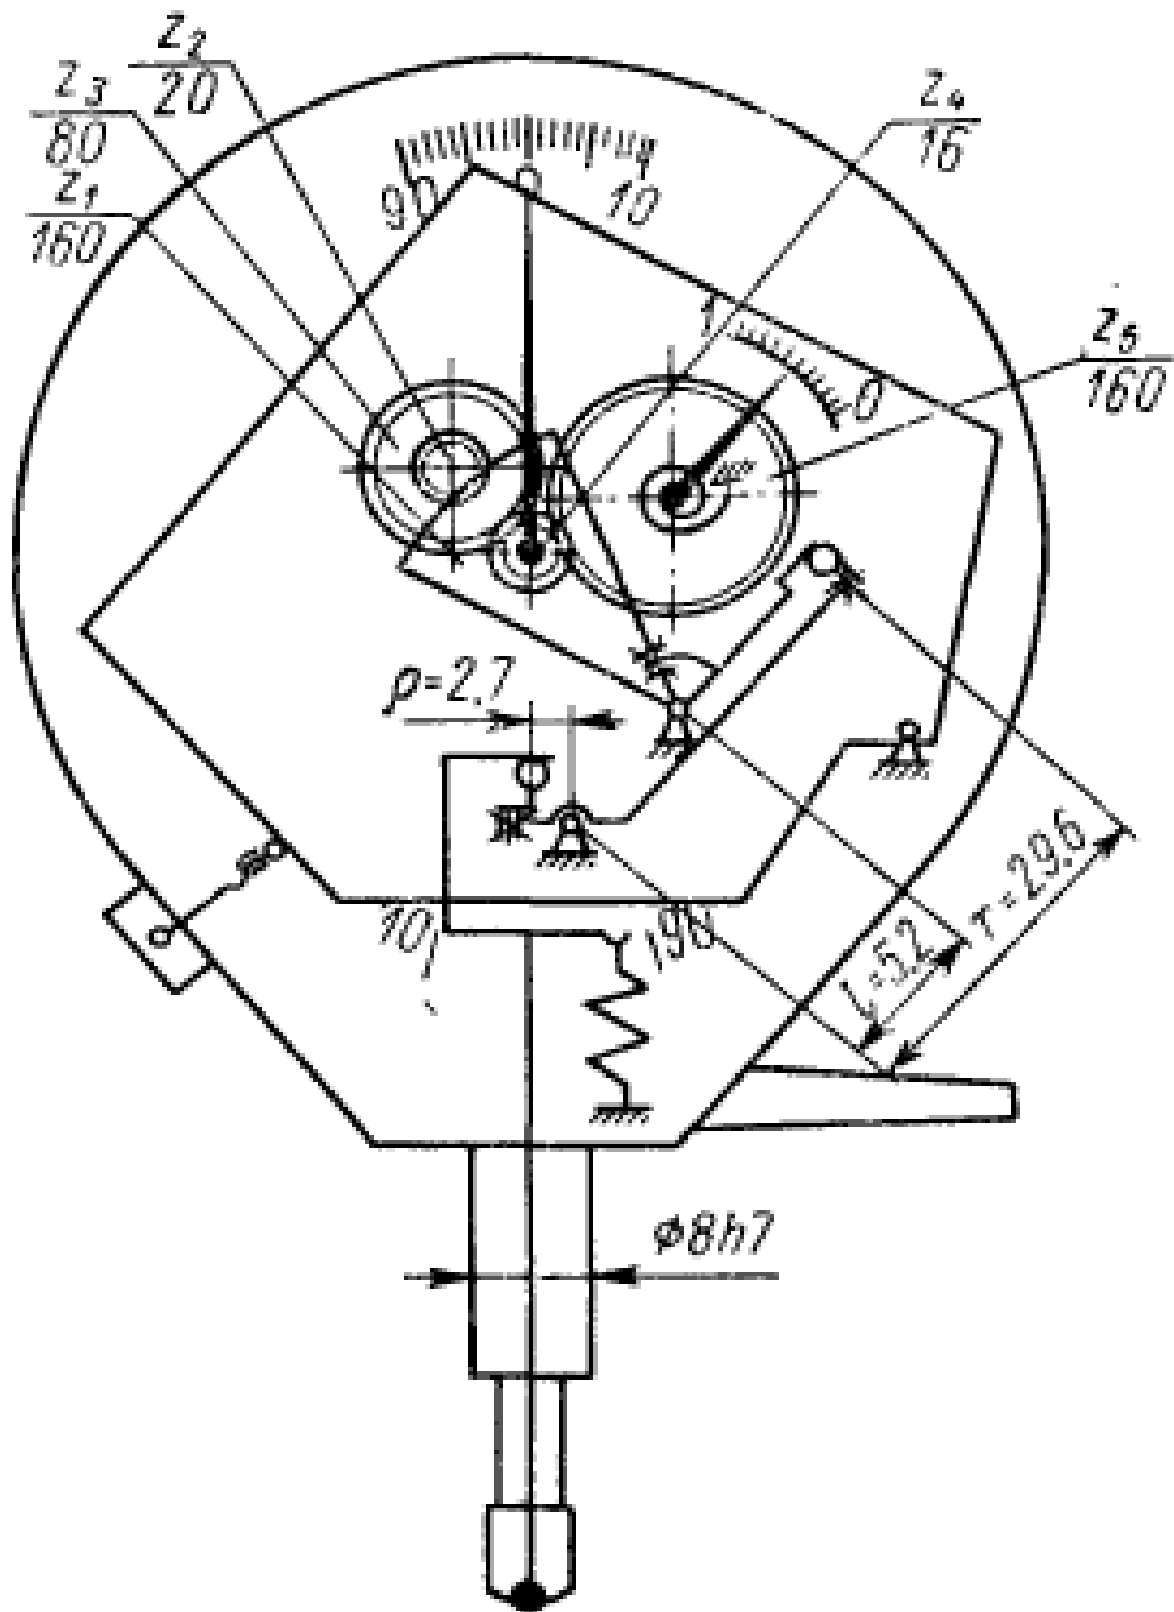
Кинематическая схема многооборотных рычажно-зубчатых измерительных головок МИГ с двухрычажной передачей
